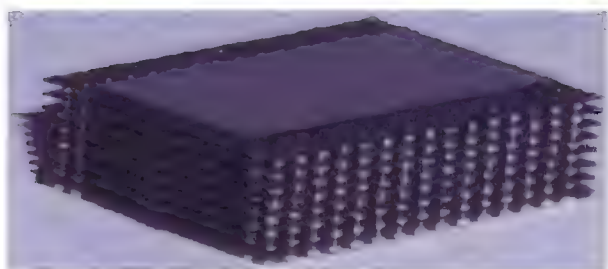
Сборка FBGA "корпус - на - корпусе"
